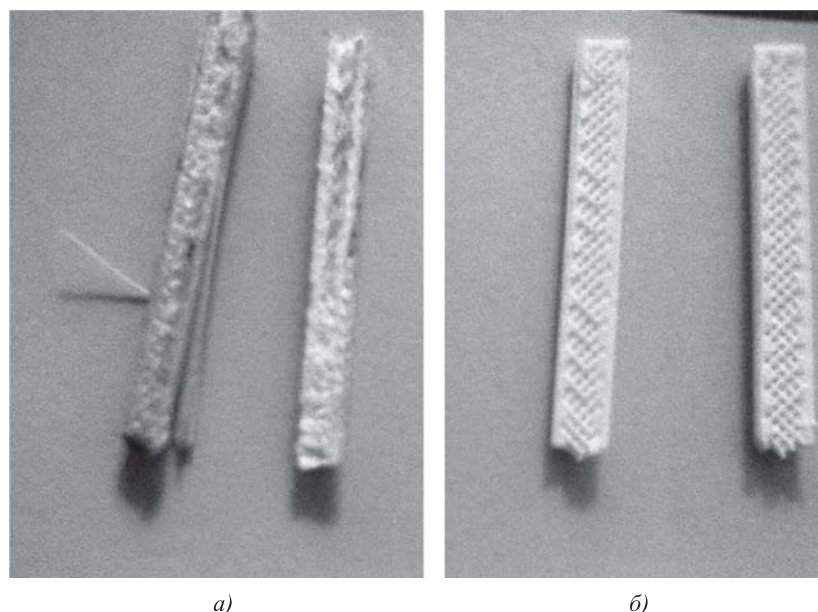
Поверхность образцов после испытаний на срез: а — контрольный образец; б — обработанный образец
